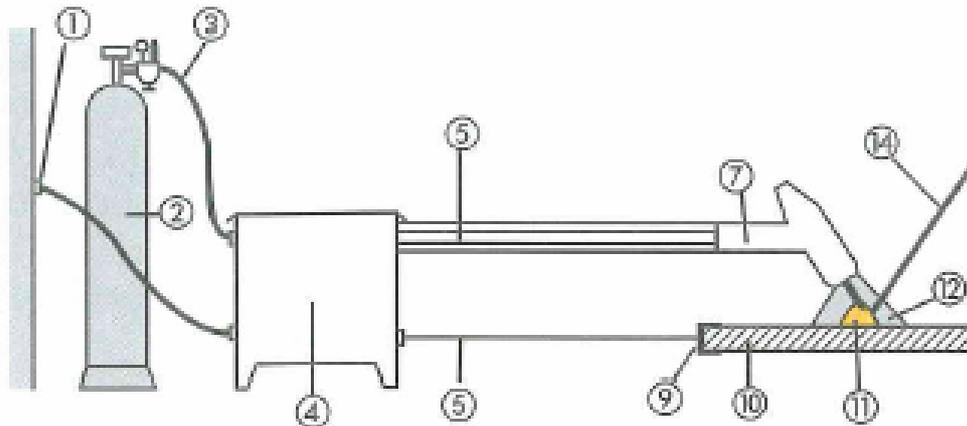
Aufbau einer WIG-Schweißanlage
